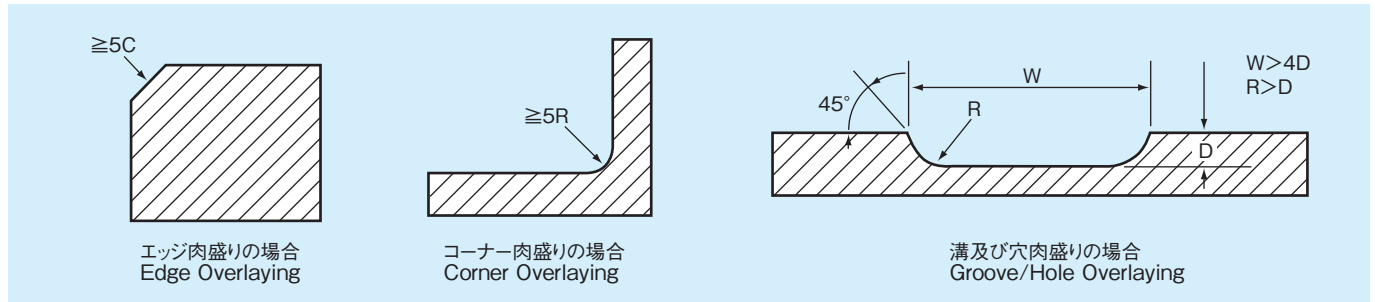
肉盛り溶接における標準開先形状 Figure 1. Standard groove shapes for overlay welding
